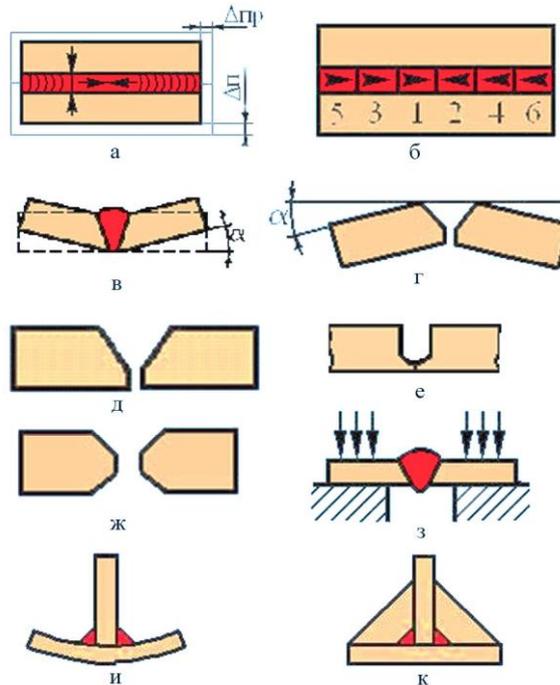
Усадка, угловая деформация сварных заготовок и способы их устранения:
